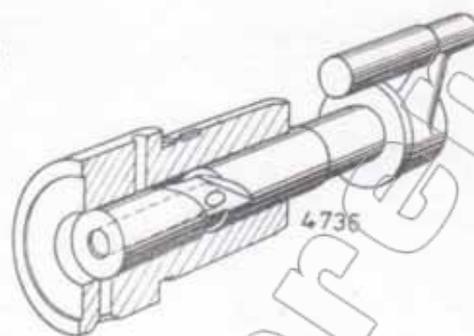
Einspritzpumpelement mit Schrägkantensteuerung
